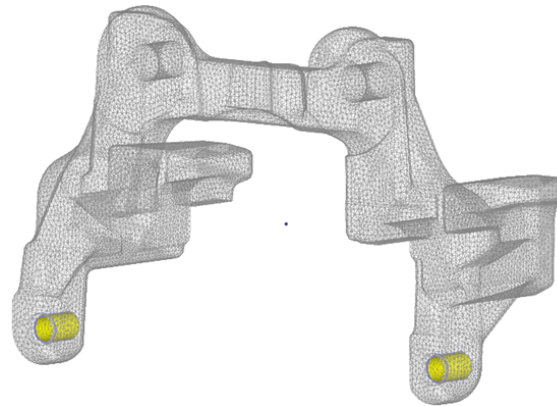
Superfície do furo em que monta o segundo componente do sistema de travagem.
